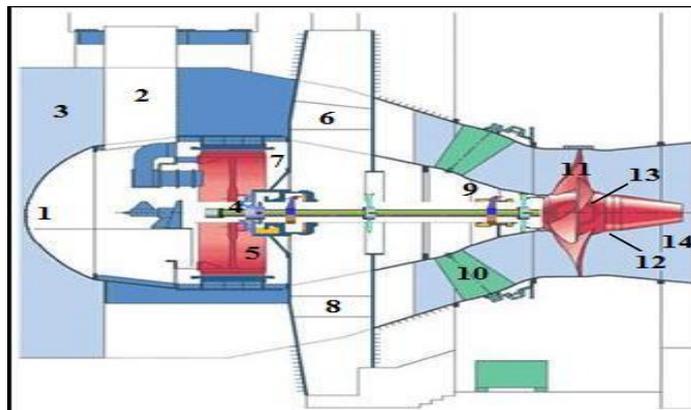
Corte e Principais Componentes da Turbina Hidráulica Tubular "Kaplan" Bulbo
